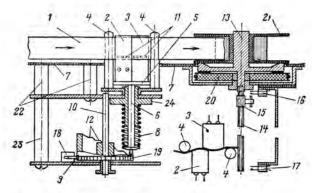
Механизм перемещения магнитных головок и приемный узел магнитофона: 1 — магнитная лента: 2 — стирающая головка; 3 — универсальная головка; 4 - направляющие стойки; 5 — пластина; 6 шток; 7 — панель лентопротяжного механизма; 8 — пружина; 9 — кулачок; 10— вал кулачка; 11— маг-нитопроводы головок; 12— ступеньки кулачка; 13 - подкатушечник приемного узла; 14 — ходовой винт; 15 — каретка; 16, 17 — концевые выключатели; 18 - электромагнит; 19 — храповое колесо; 20 — шкив приемного узла: 21 — приемная катушка; 22, 23 — стойки.
